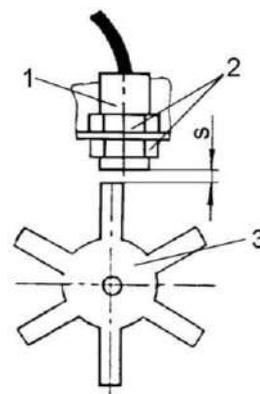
Регулировка механизма управления скоростью движения
